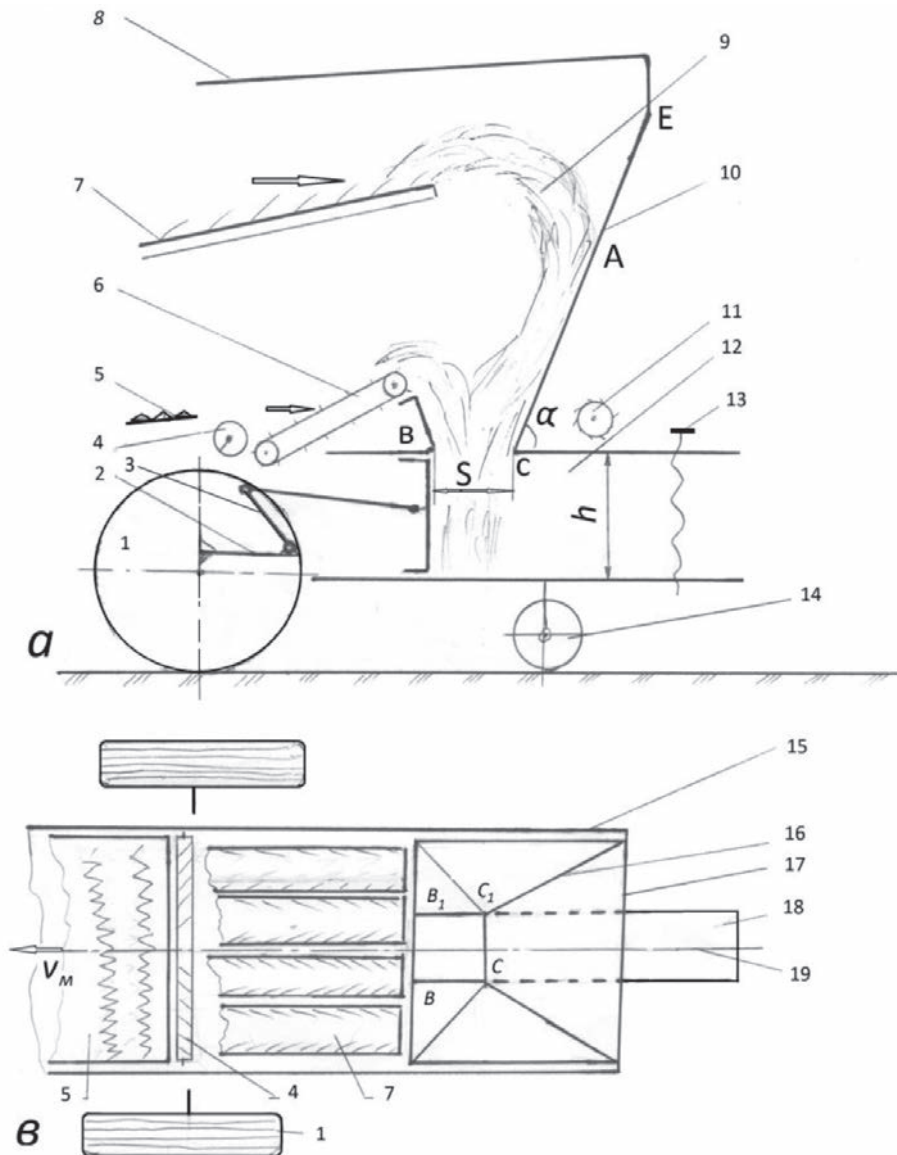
Схема установки соломопрессующего аппарата вместо соломоизмельчителя и разбрасывателя на комбайн Dominator 130: *a* – вид сбоку; *б* – вид сверху; 1 – заднее колесо комбайна; 2 – балка для крепления соломоизмельчающего и разбрасывающего устройств; 3 – кривошип привода соломопрессующего поршня; 4 – шнек для транспортировки половы мелких примесей, сходящих с верхнего решета; 5 – верхнее решето; 6 – ленточный транспортер; 7 – клавиша соломотряса; 8 – крыша комбайна; 9 – траектория схода соломы с соломотряса; 10 – щиток-направитель; 11 – привод вязального аппарата; 12 – прессовальная камера; 13 – регулятор плотности тюков; 14 – опорное колесо тележки прессующего аппарата; 15 – боковина комбайна; 16 – щиток-направитель; 17 – задний щиток; 18 – сход с соломопрессующего аппарата; 19 – ось симметрии комбайна
